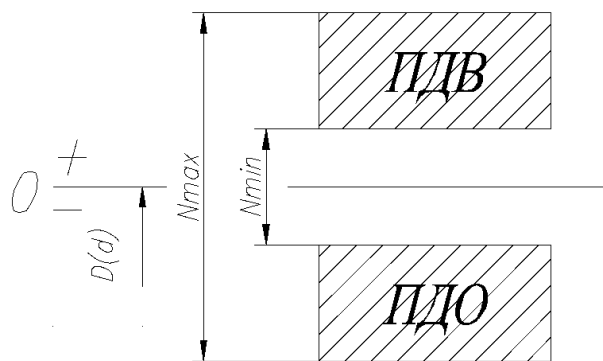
Схема розташування полів допусків з'єднання з натягом
